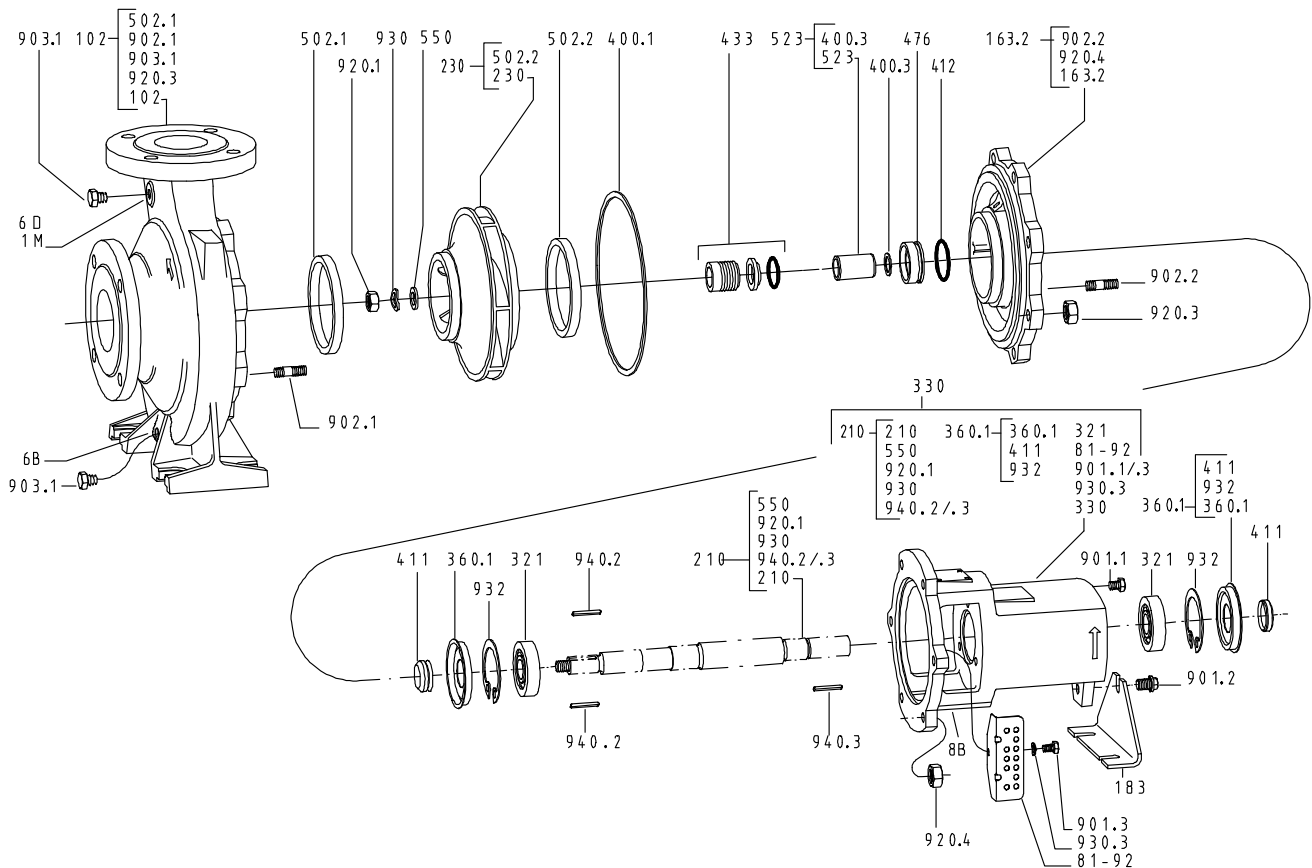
Etanorm со стандартным торцовым уплотнением и резьбовой крышкой корпуса
